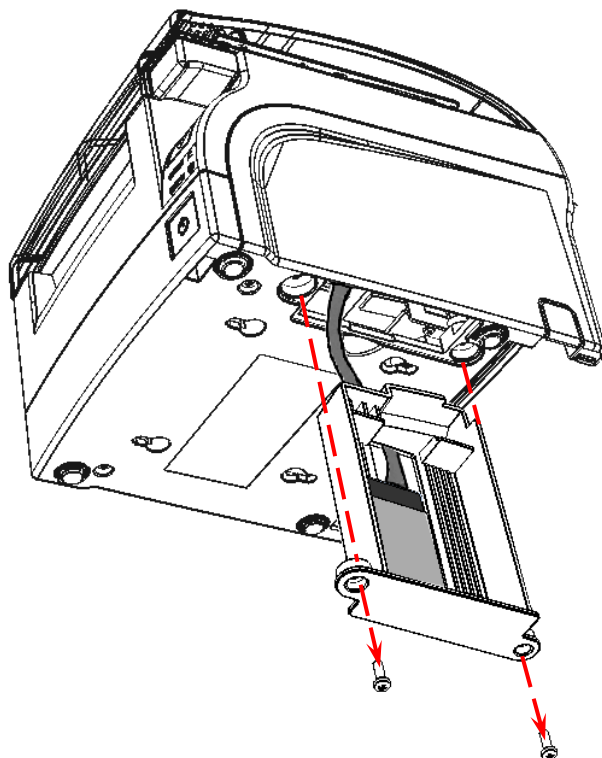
Извлечение отсека для ФН из корпуса ККТ
